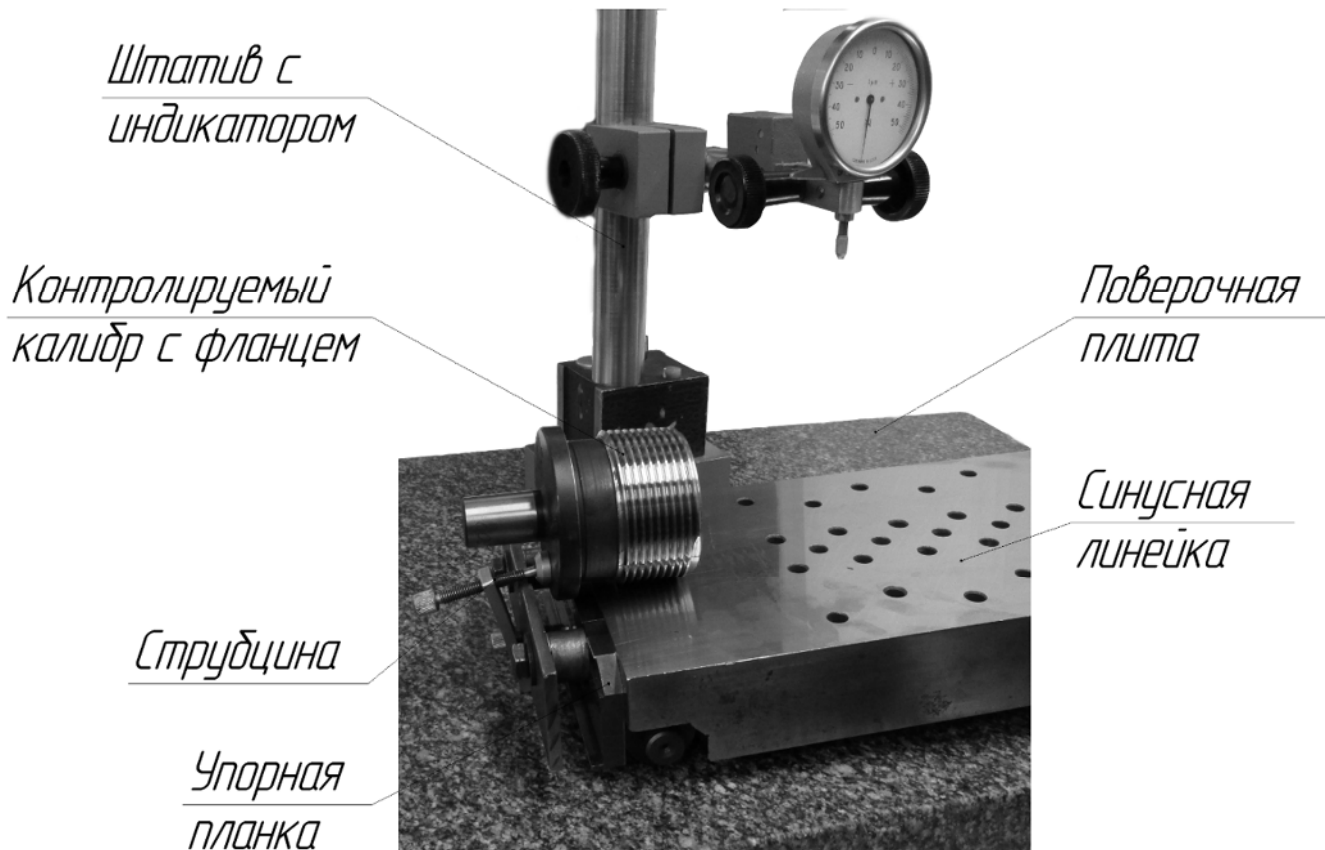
Установка калибра-пробки с фланцем на синусной линейке
